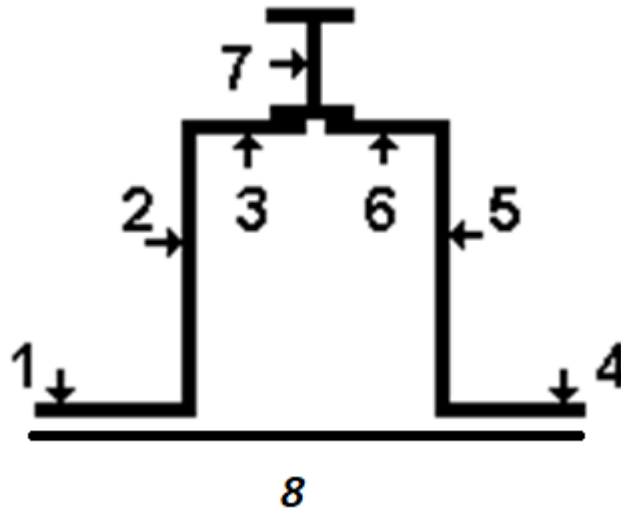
Розрахункова схема рами критого вагона моделі 12-9745 на поздовжнє і поперечне навантаження
